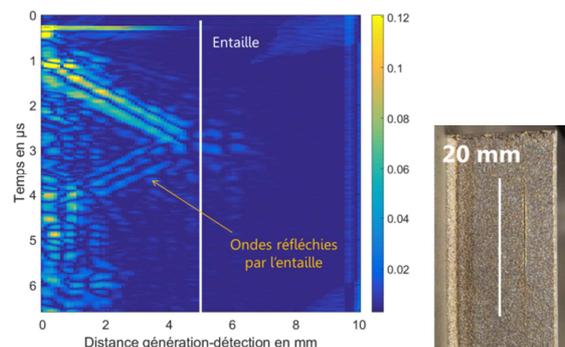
Détection d'un défaut réel sur pièce rugueuse par UL
